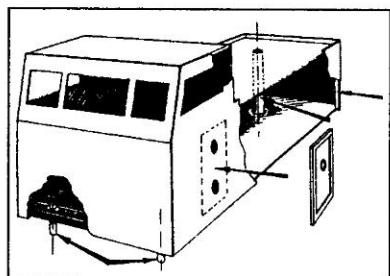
Подкрепление паяного сборочного узла уголками и трубками
